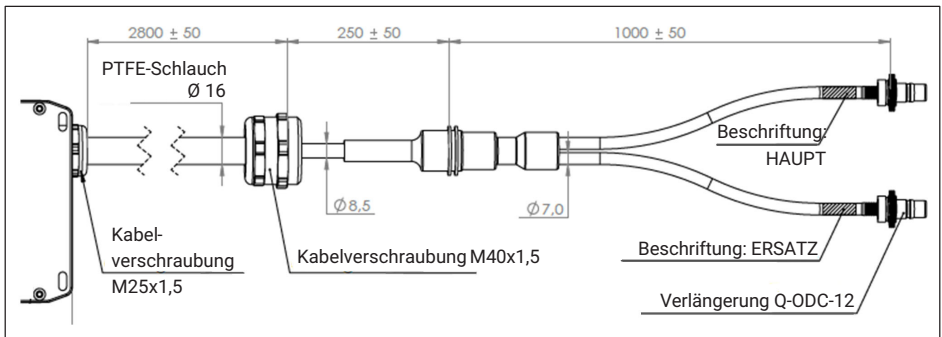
Anschlussbox – Kabelseite – technische Zeichnung (Abmessungen in mm)
